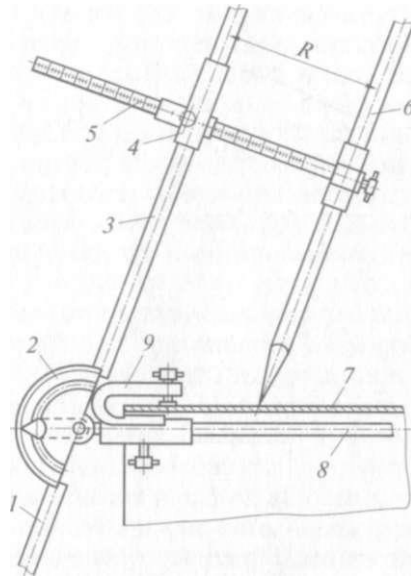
Приспособление для I разметки линий пересечения труб под углом 20...90°:
